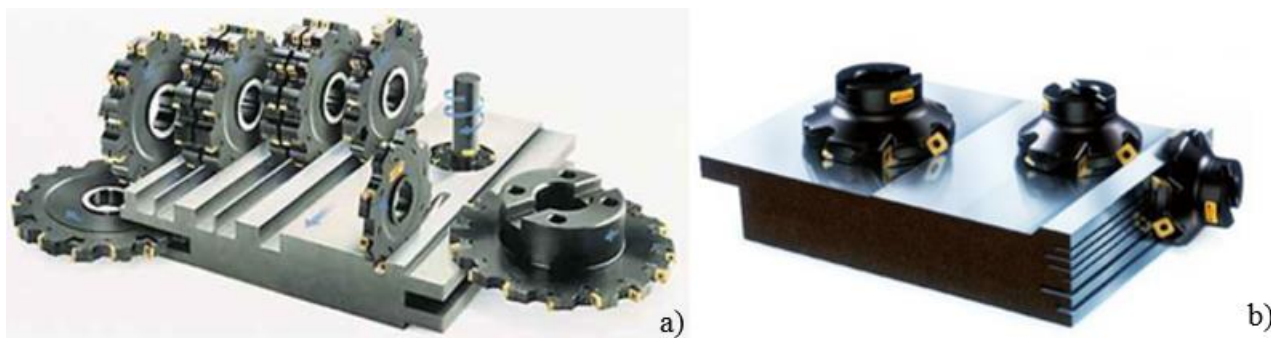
Tipos de operações de fresamento: (a) tangencial ou periférico, (b) frontal ou de topo. (SANDVIK COROMANT, 2010)
